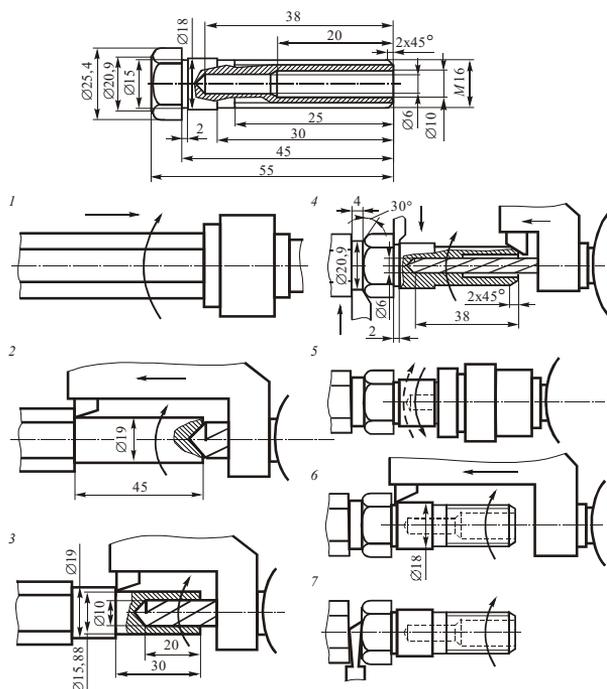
Схема обработки детали на токарно-револьверном станке-автомате:
